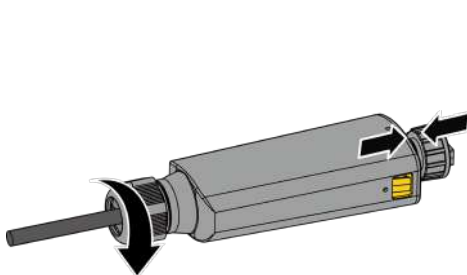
Dichtung anbringen und Kabelverschraubung anziehen
